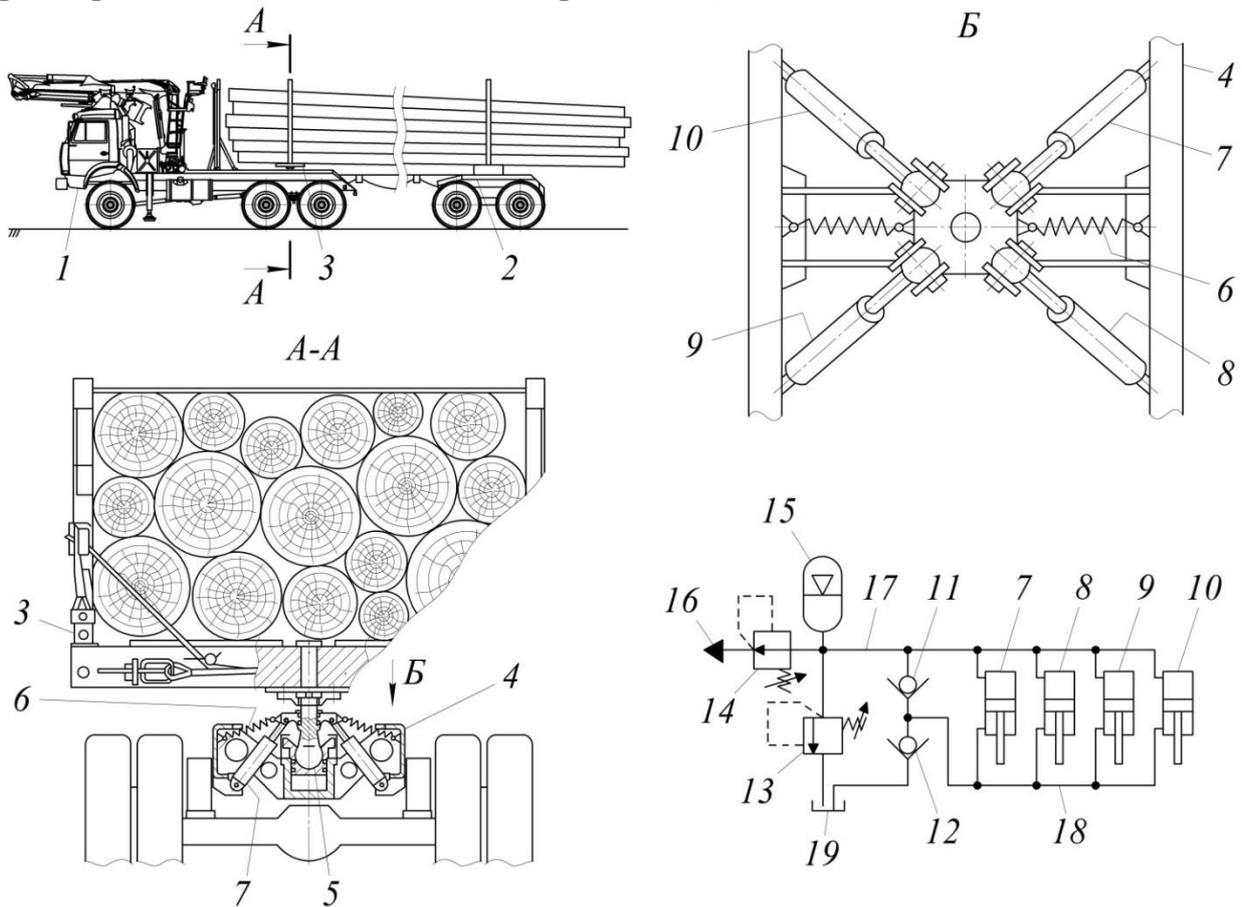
Схема рекуперативного поворотного коникового устройства с шаровой опорой
